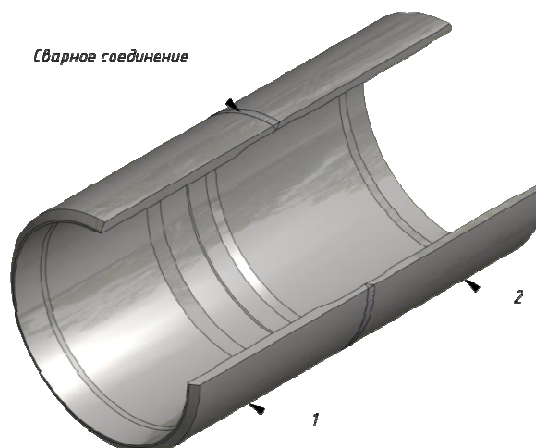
Конструкция переходника: 1 – патрубок из стали перлитного класса; 2 – патрубок из стали аустенитного класса
